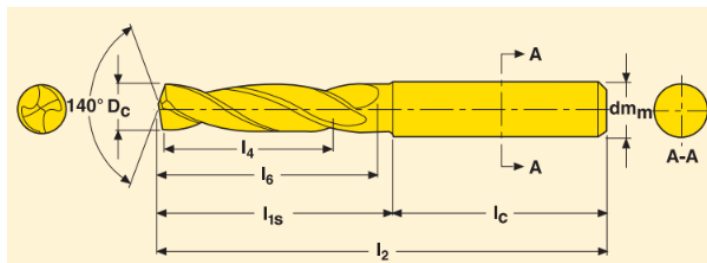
Свердло SD1103-0420-017-06R1 [14, с.25]
